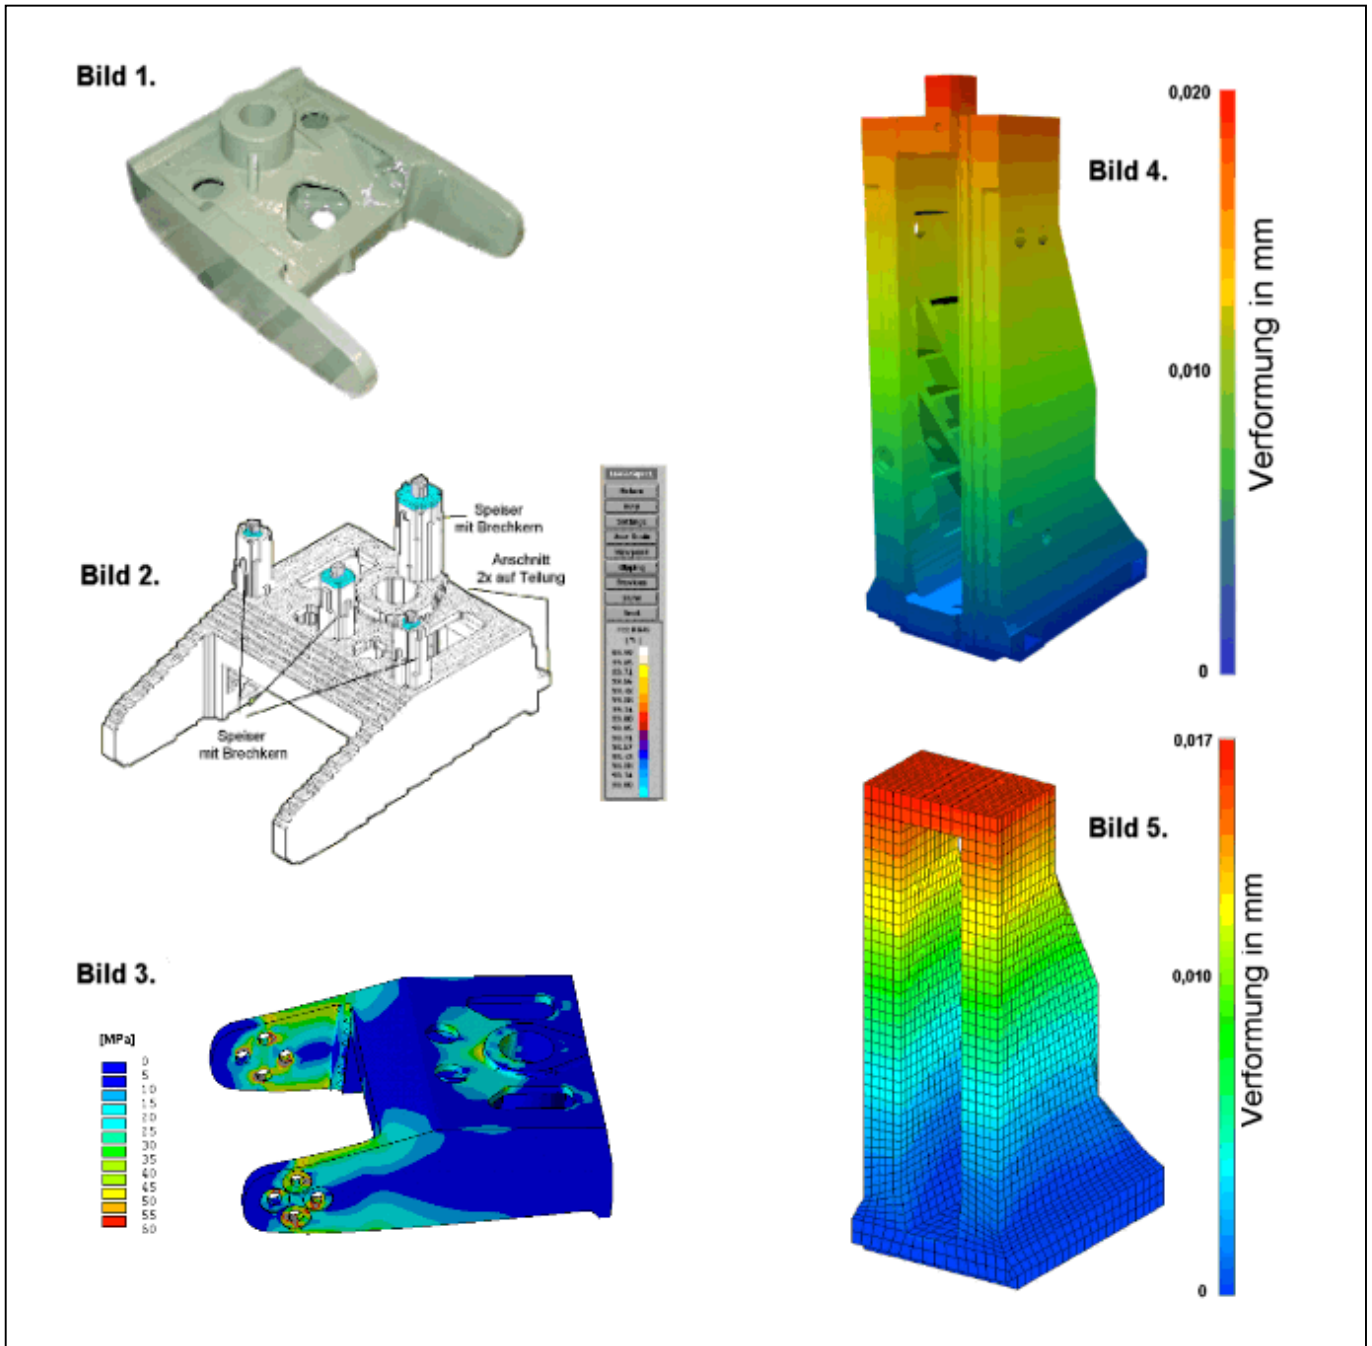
Bauteil für Blasformmaschine vor der Bearbeitung
